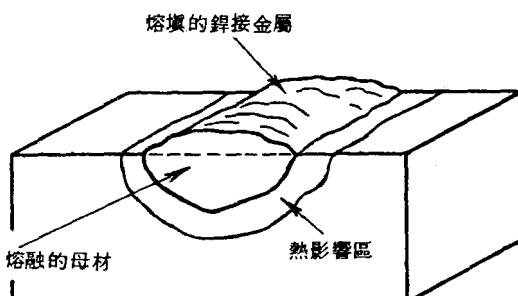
鋸道的截面即為鋸塊 (weld nugget)，截面積就是鋸塊面積 (weld nugget area)
